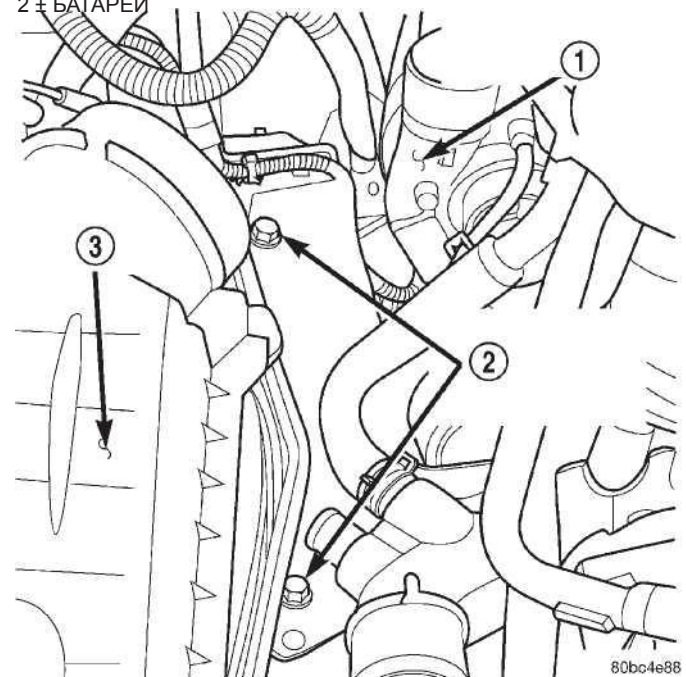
Болты пластины подоконника опоры двигателя - Rightside
